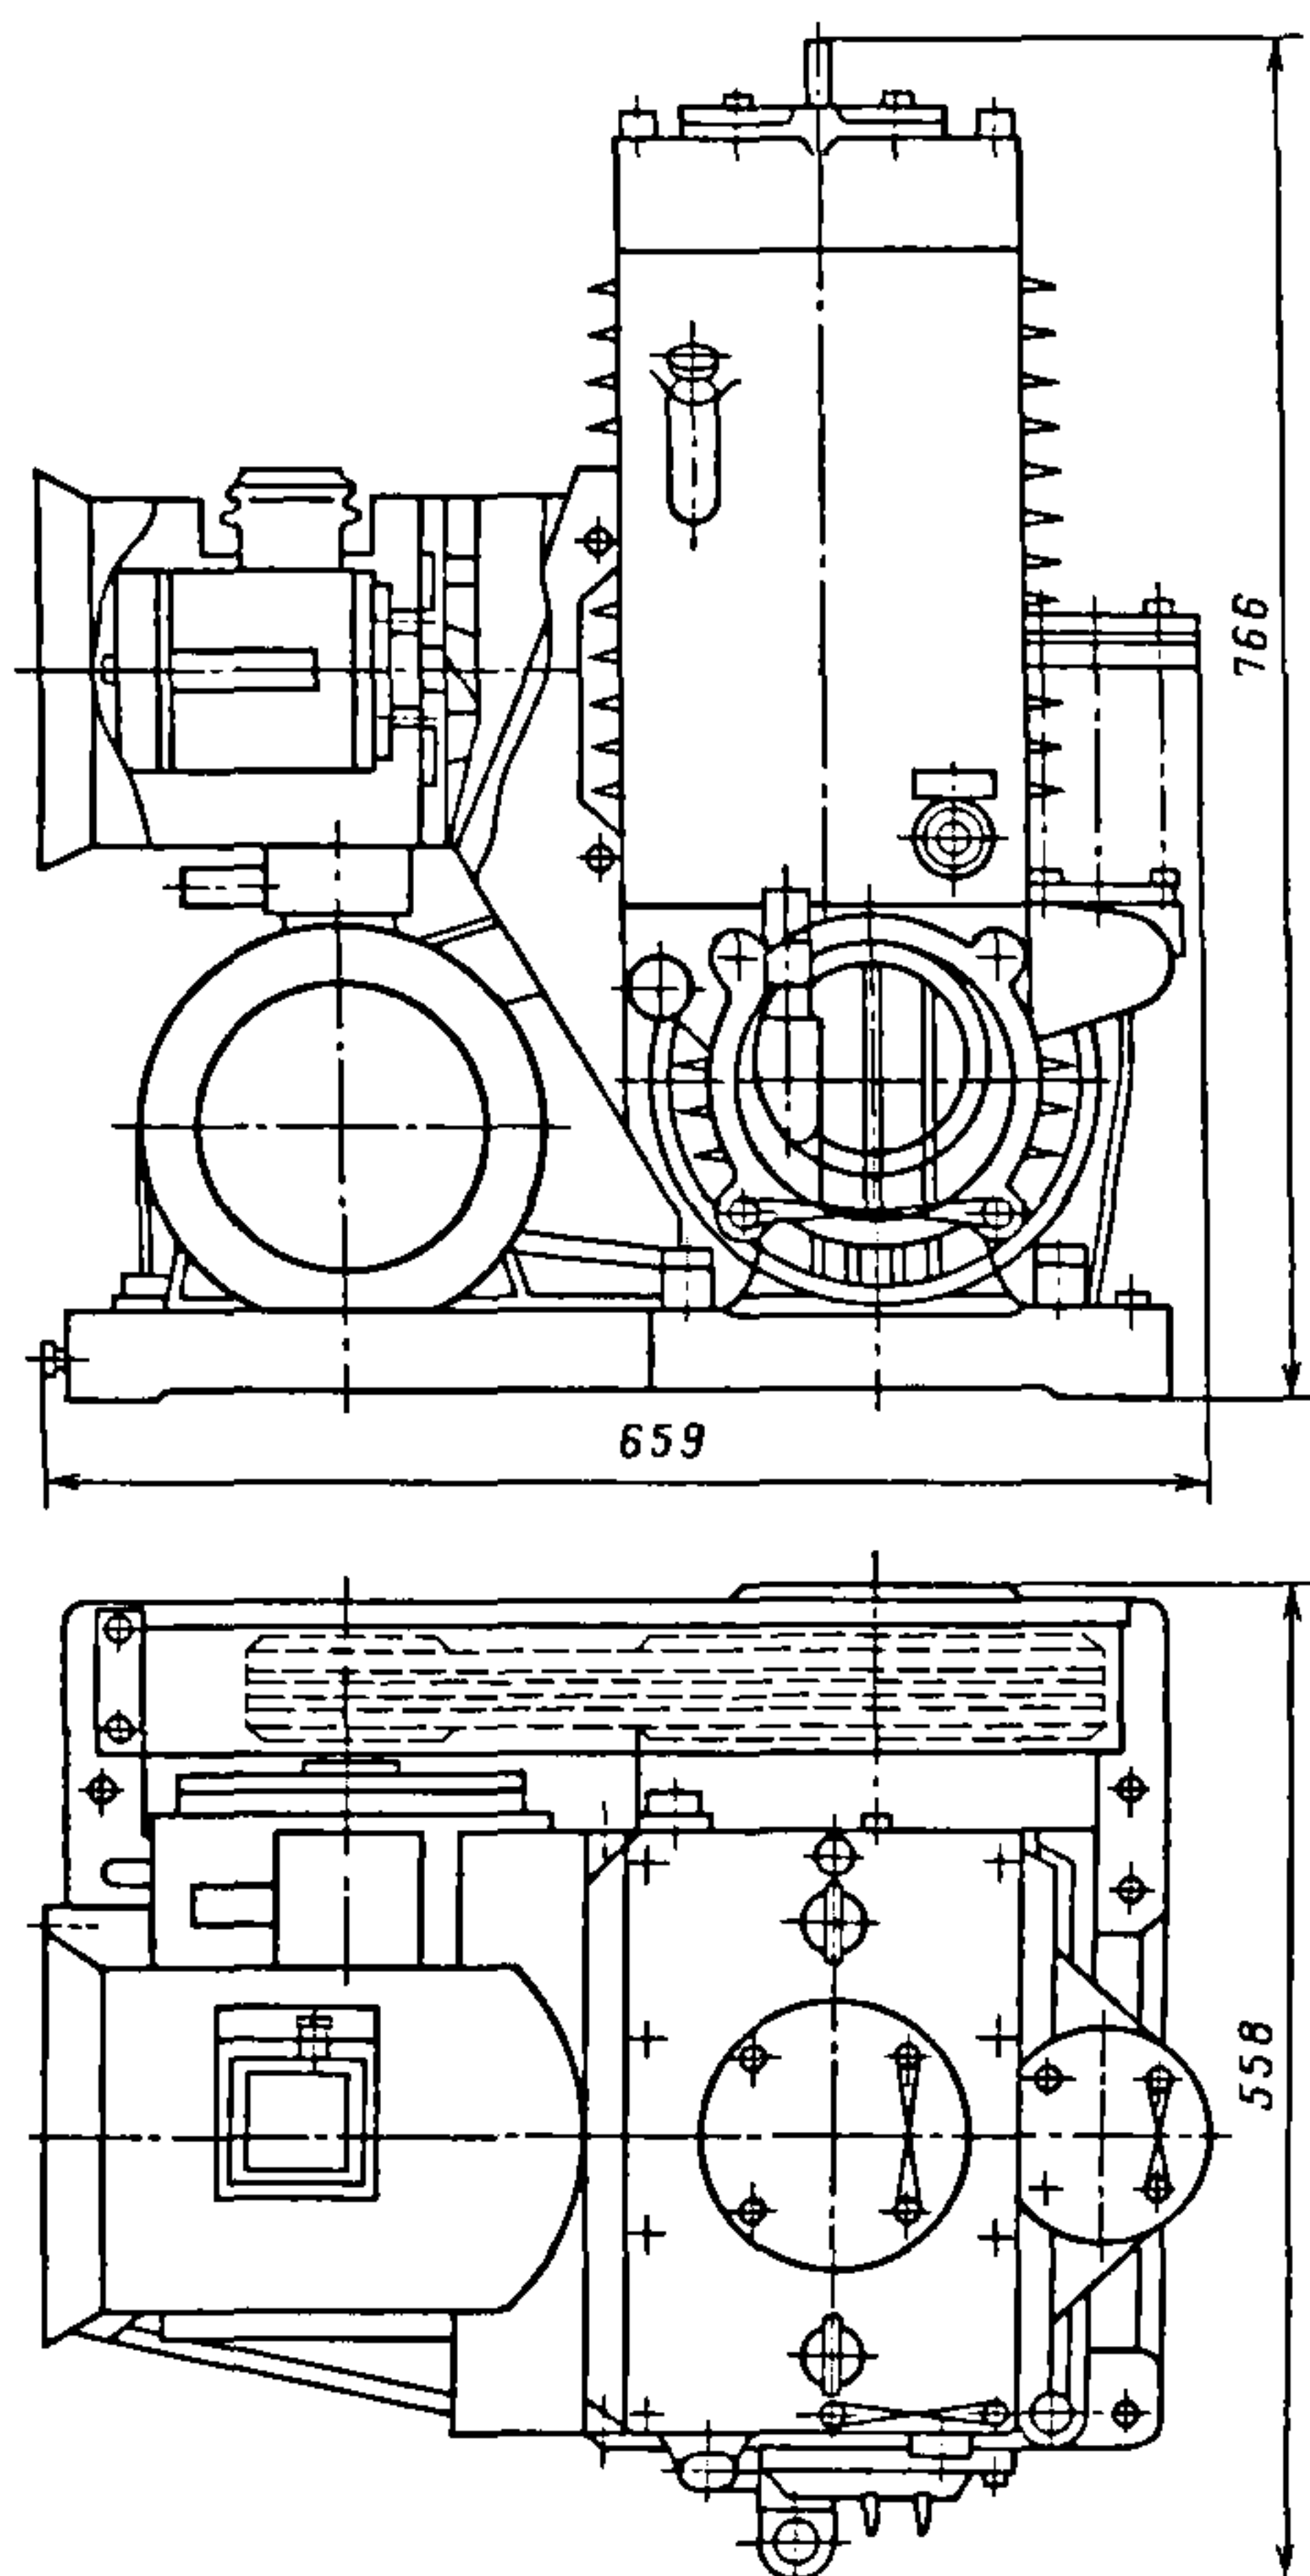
Габаритный чертеж вакуумного насоса НВР-20С
